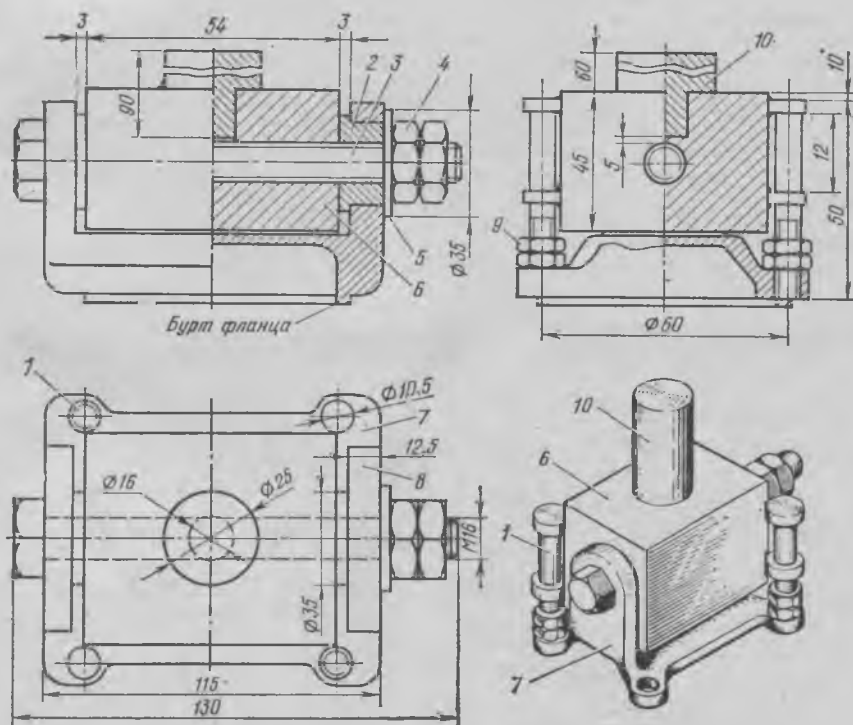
Приспособление для обработки бурта фланца карданного вала вентилятора охлаждения генератора на токарном станке после сварки:
